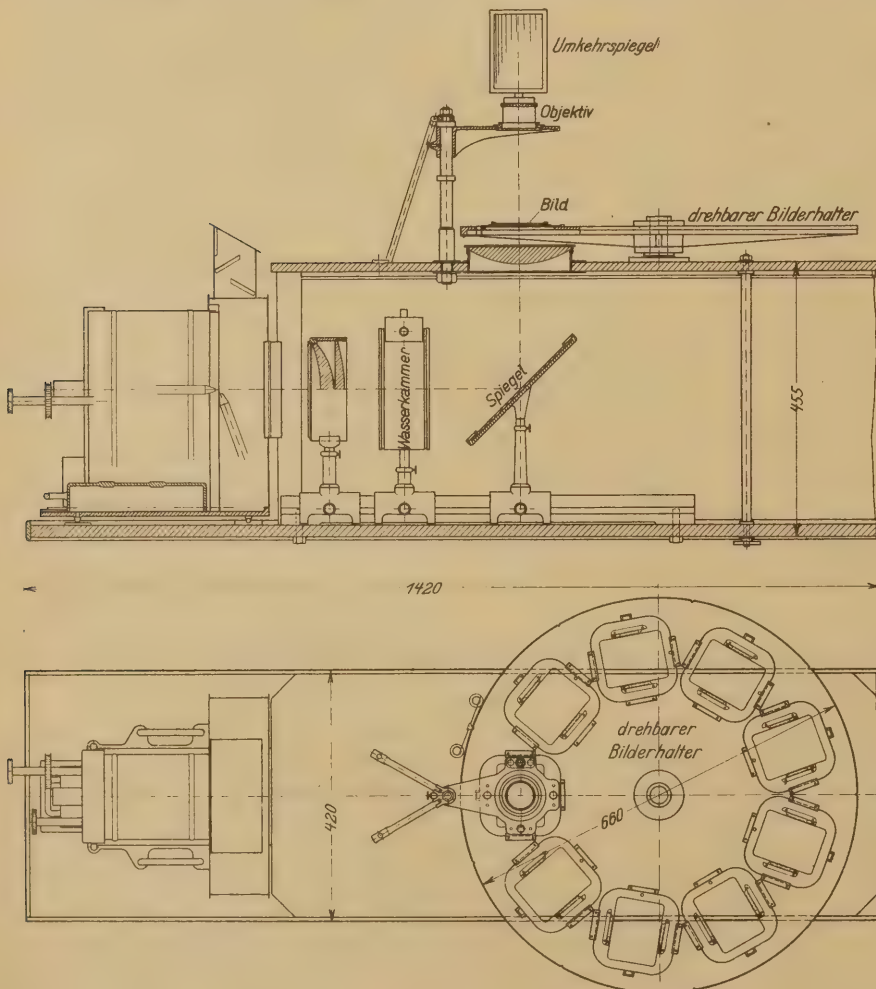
und 2. Aufriß und Grundriß des Bildwerfers mit drehbarem Bilderhalter.
